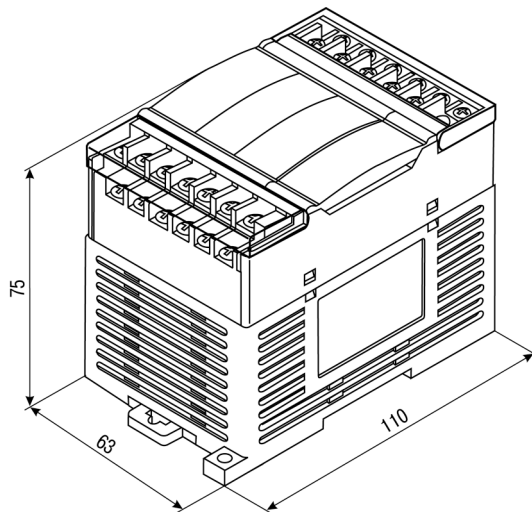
Габаритный чертеж ОВЕН ПР110-х.8х.4х
